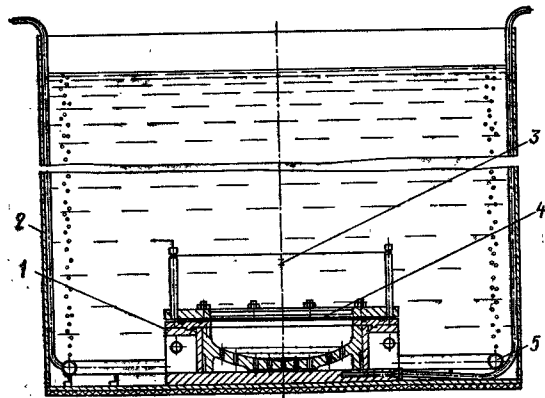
Установка для взрывной штамповки с воздушно-пузырьковой защитой:
